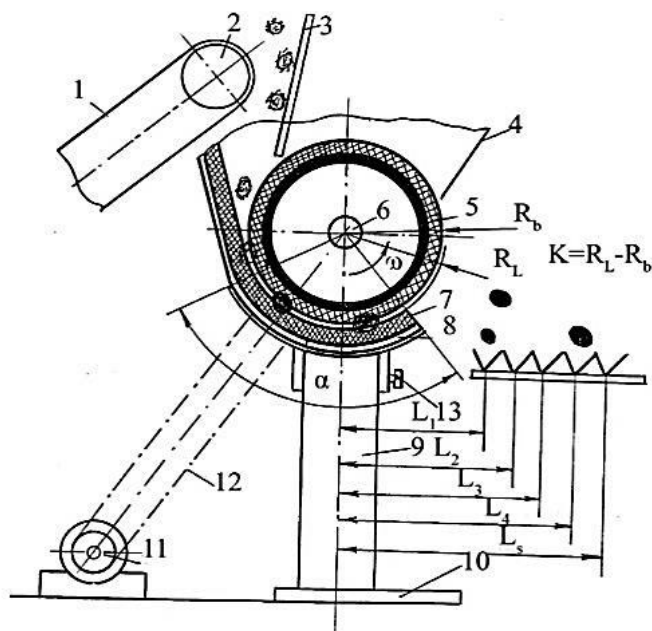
Техническое средство для протравливания семян сельскохозяйственных растений: 1 — лента транспортера; 2 — барабан транспортера; 3 — направляющий; 4 — бак; 5 — протравливающий барабан с поверхностью, покрытый поролоном; 6 — вал протравливающего барабана; 7 — поролоновая лента; 8 — посуда; 9 — звено; 10 — стойка; 11 — электродвигатель; 12 — цепная передача; 13 — болт
